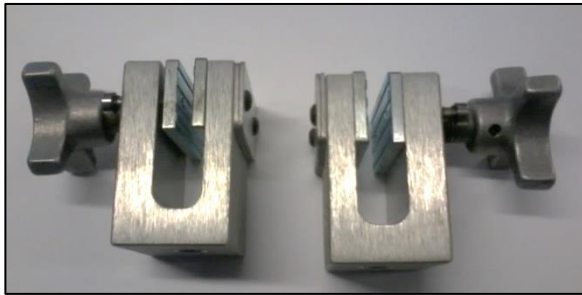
Mordazas de la máquina Universal de ensayo de tensión/compresión.
